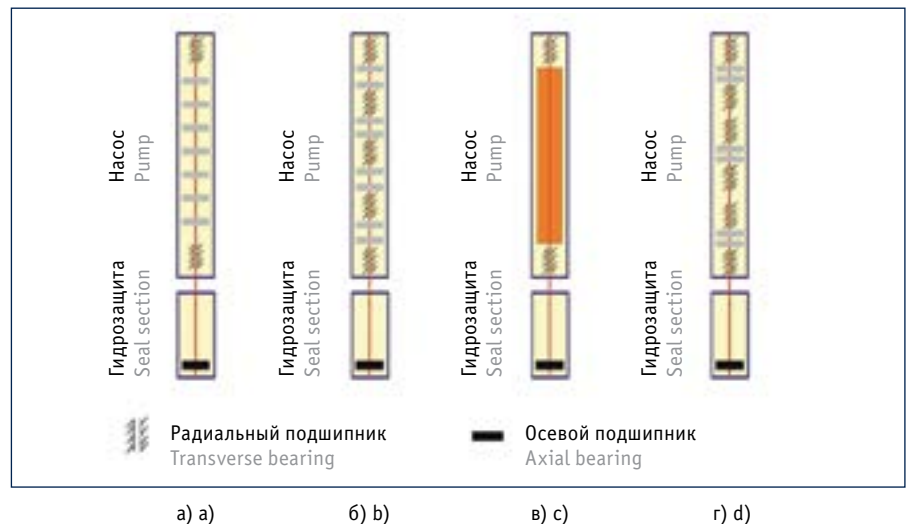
Схемы сборки лопастного насоса для добычи нефти [7]:
